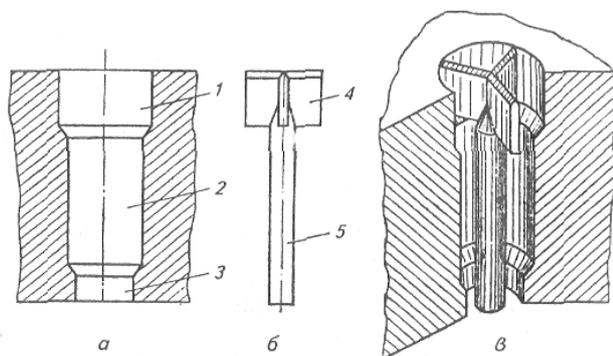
Формующее отверстие дисковой матрицы с вкладышем: а – профиль отверстия; б – вкладыш трехпорный; в – отверстие с запрессованным вкладышем в сборе
